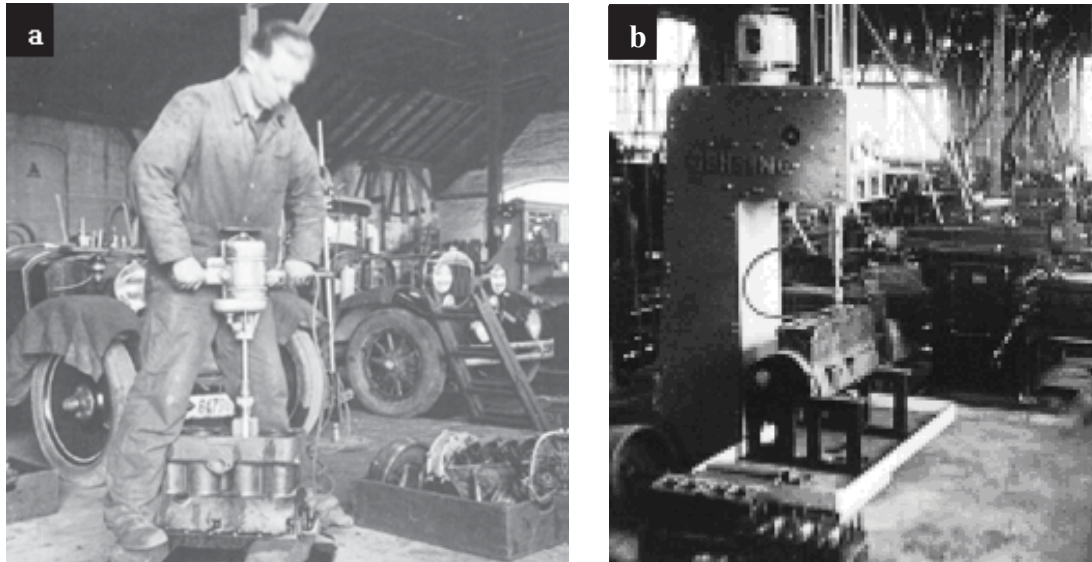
(a) Photo d'une opération de rodage manuel. (b) Machine de rodage mécanisée de type Gehring.
